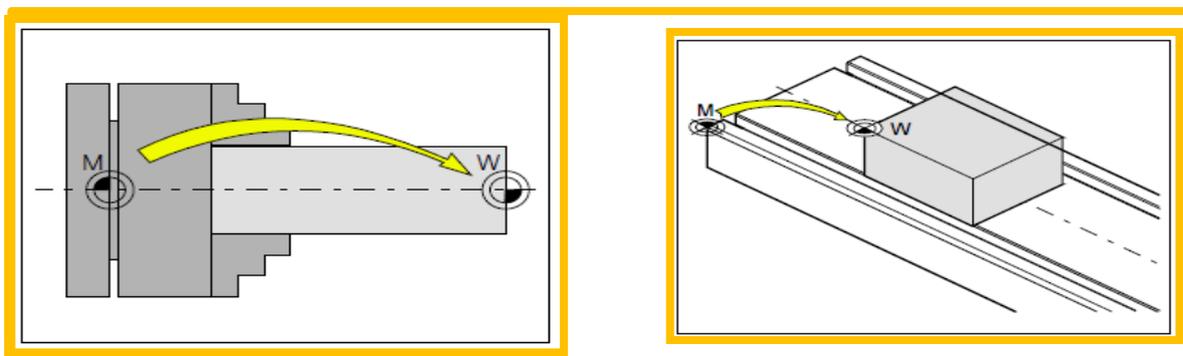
Décalage d'origine machine M à l'origine de la pièce W dans le tournage et fraisage.[2]
